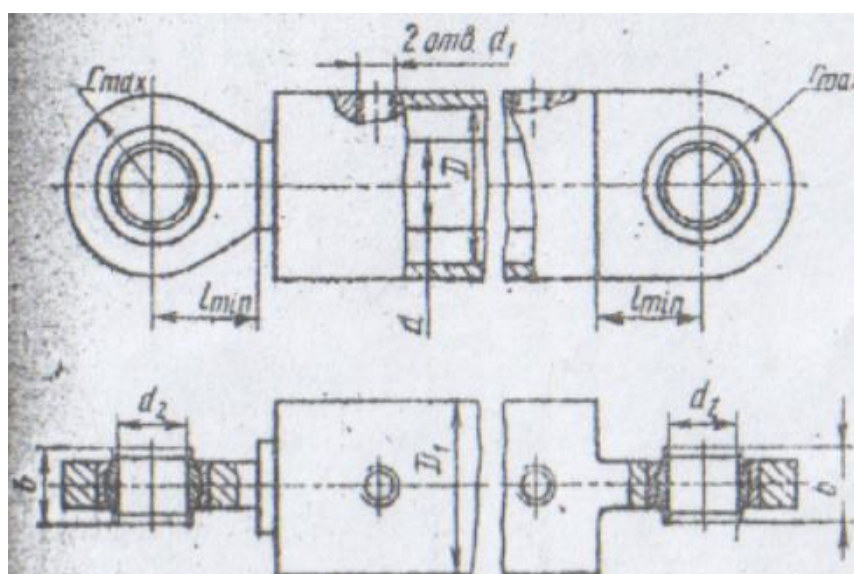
Чертеж гидроцилиндра 1.16.0.Y – 40x25x63
